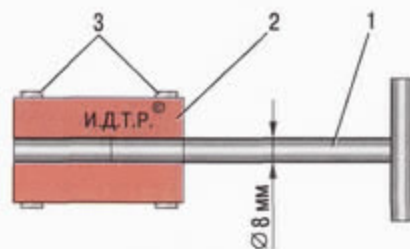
Приспособление для притирки клапанов: 1 - металлический стержень; 2 - резиновый шланг; 3 - винтовые хомуты
